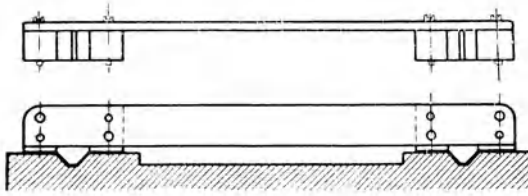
Hobellehre für ein Werkzeugmaschinenbett.
